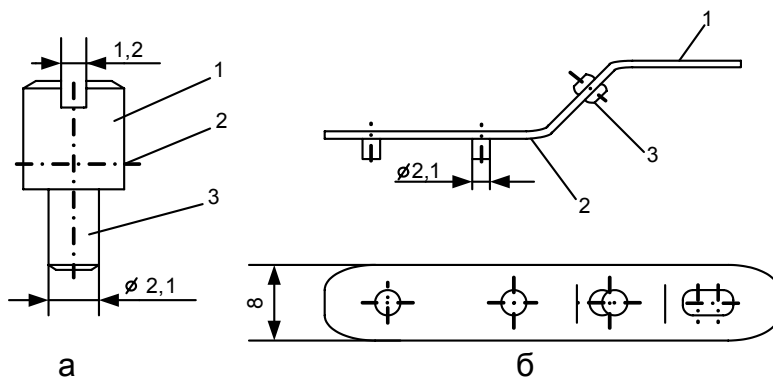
Біметалеві контакти: а – контакти типу “стовпчик”; б – пластинчастий контакт: 1 – мідь, покрита припоєм ПОС 61; 2 – алюмінієвий сплав; 3 – місце зварювання
